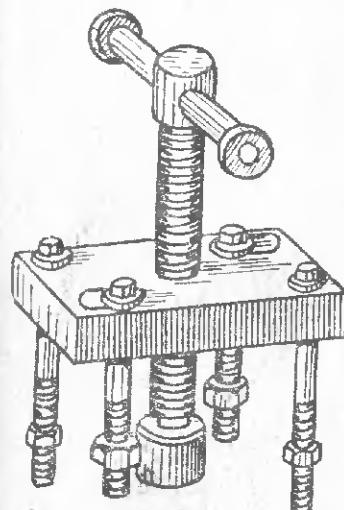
Приспособление для снятия маховика и корпуса заднего подшипника
